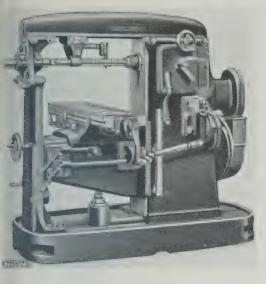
bis 6 Gute Beispiele unfallsicherer Werkzeugmaschinen.
